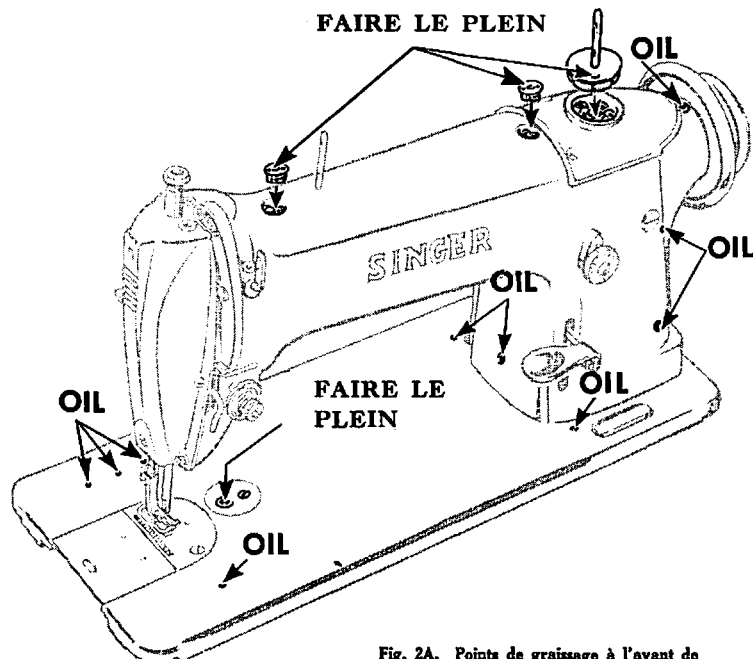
A. Points de graissage à l'avant de la Machine 196K205
